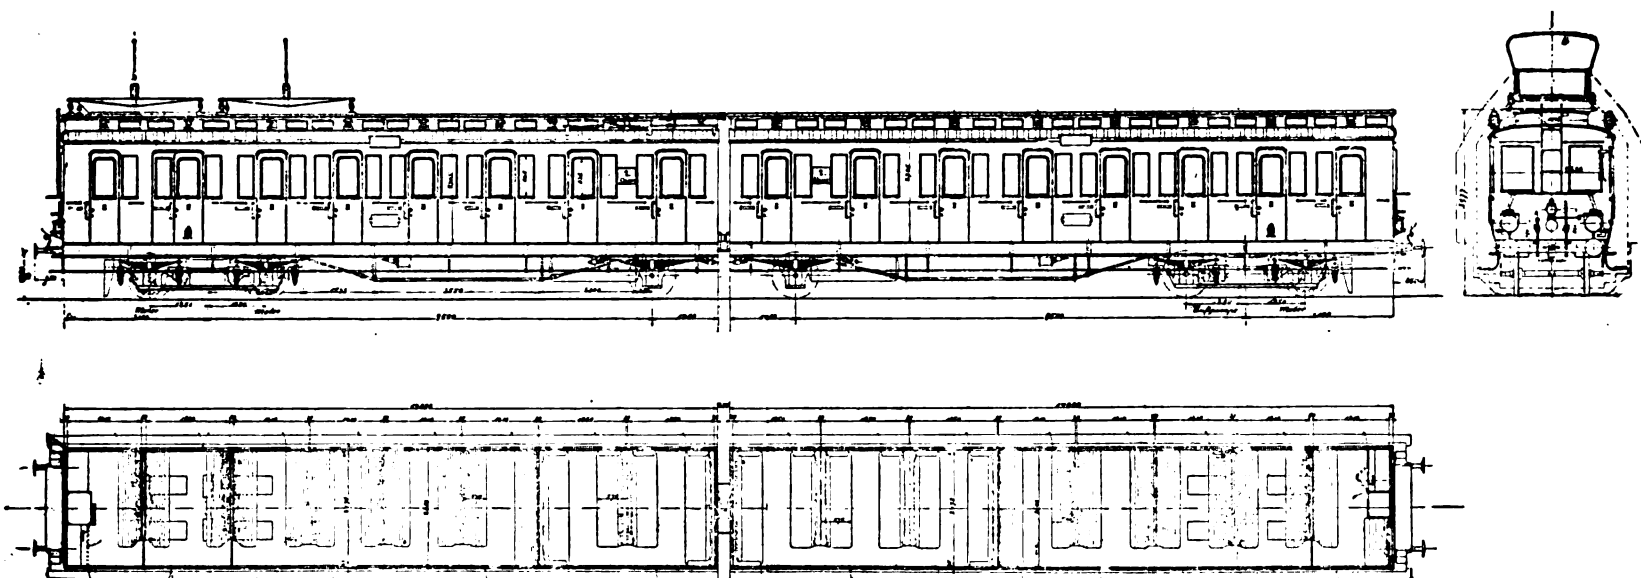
Carrozza automotrice a sei assi per la ferrovia elettrica monofase Blankenese-Ohlsdorf.
